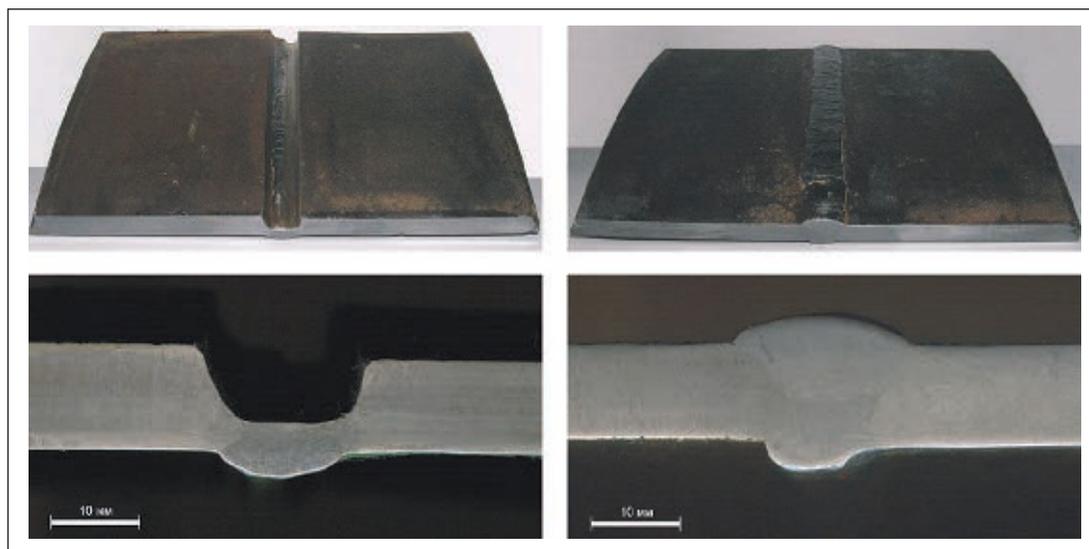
Макрошлифы стыкового соединения труб, выполненного автоматической дуговой сваркой порошковой проволокой с принудительным формированием шва за два прохода
